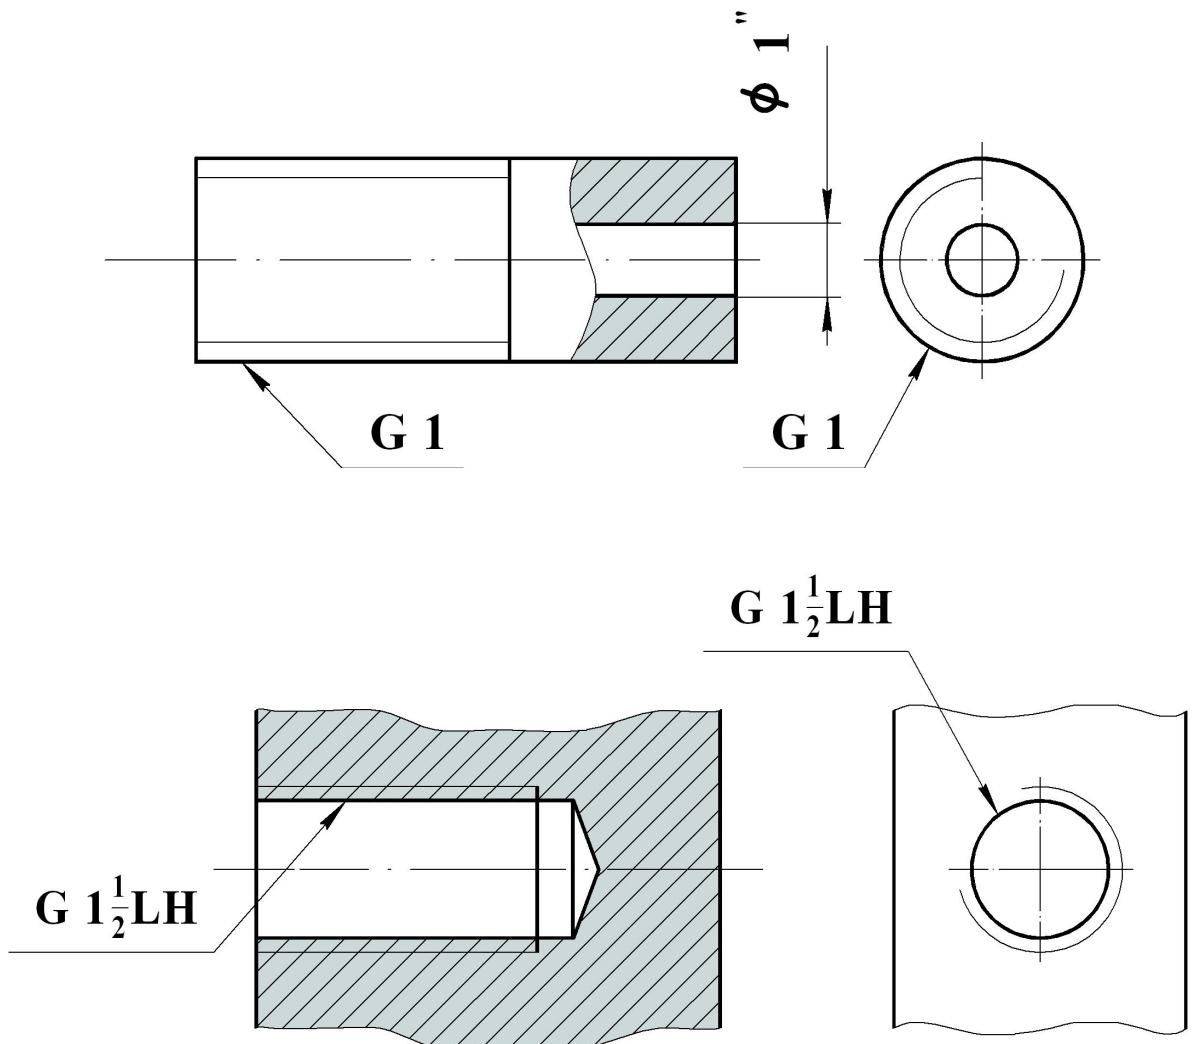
Обозначение цилиндрической трубной резьбы
